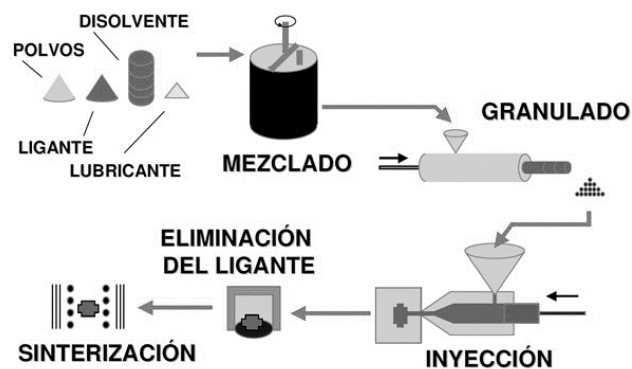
Proceso moldeo por fundición de metal. Fuente: [125]
